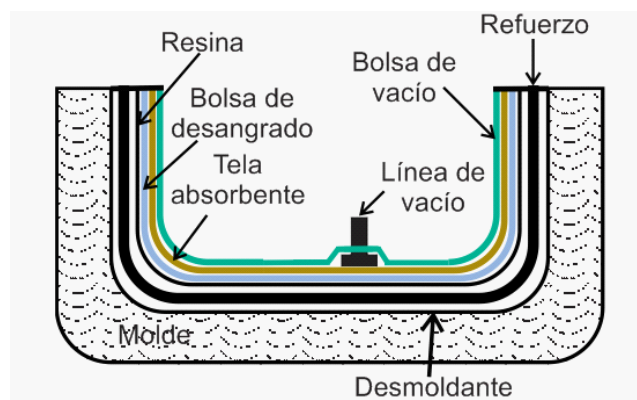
Proceso de moldeo por vacío de una pieza de PRF.
